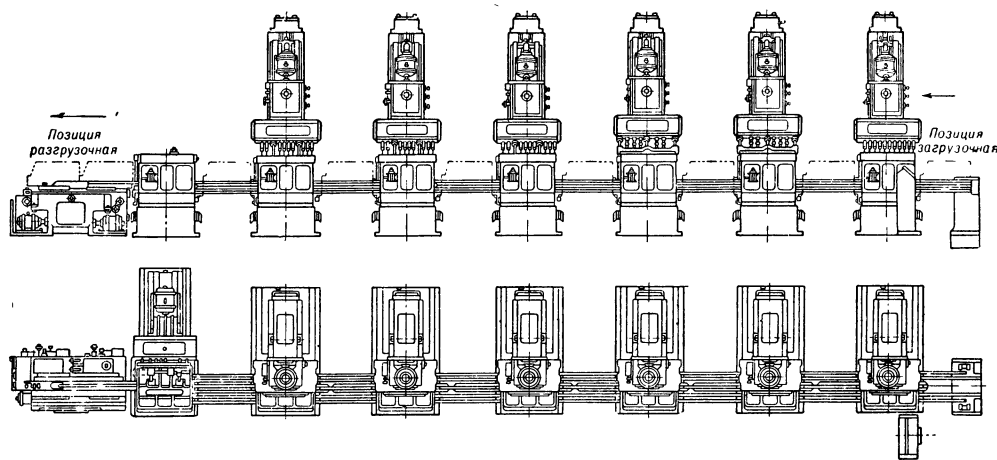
Участок автоматич. линии из агрегатных станков для обработки блока цилиндров двигателя автомобиля.
